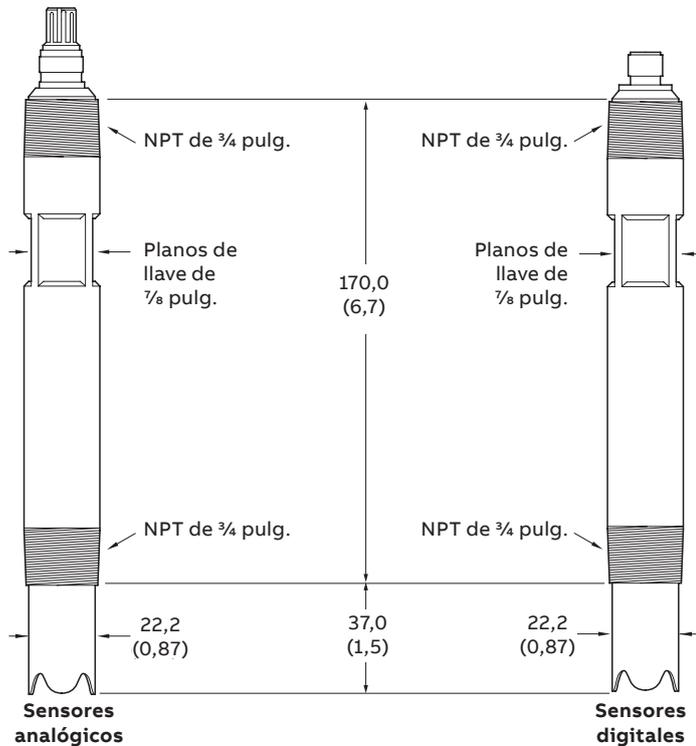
Dimensiones del cuerpo del sensor con resaltes
